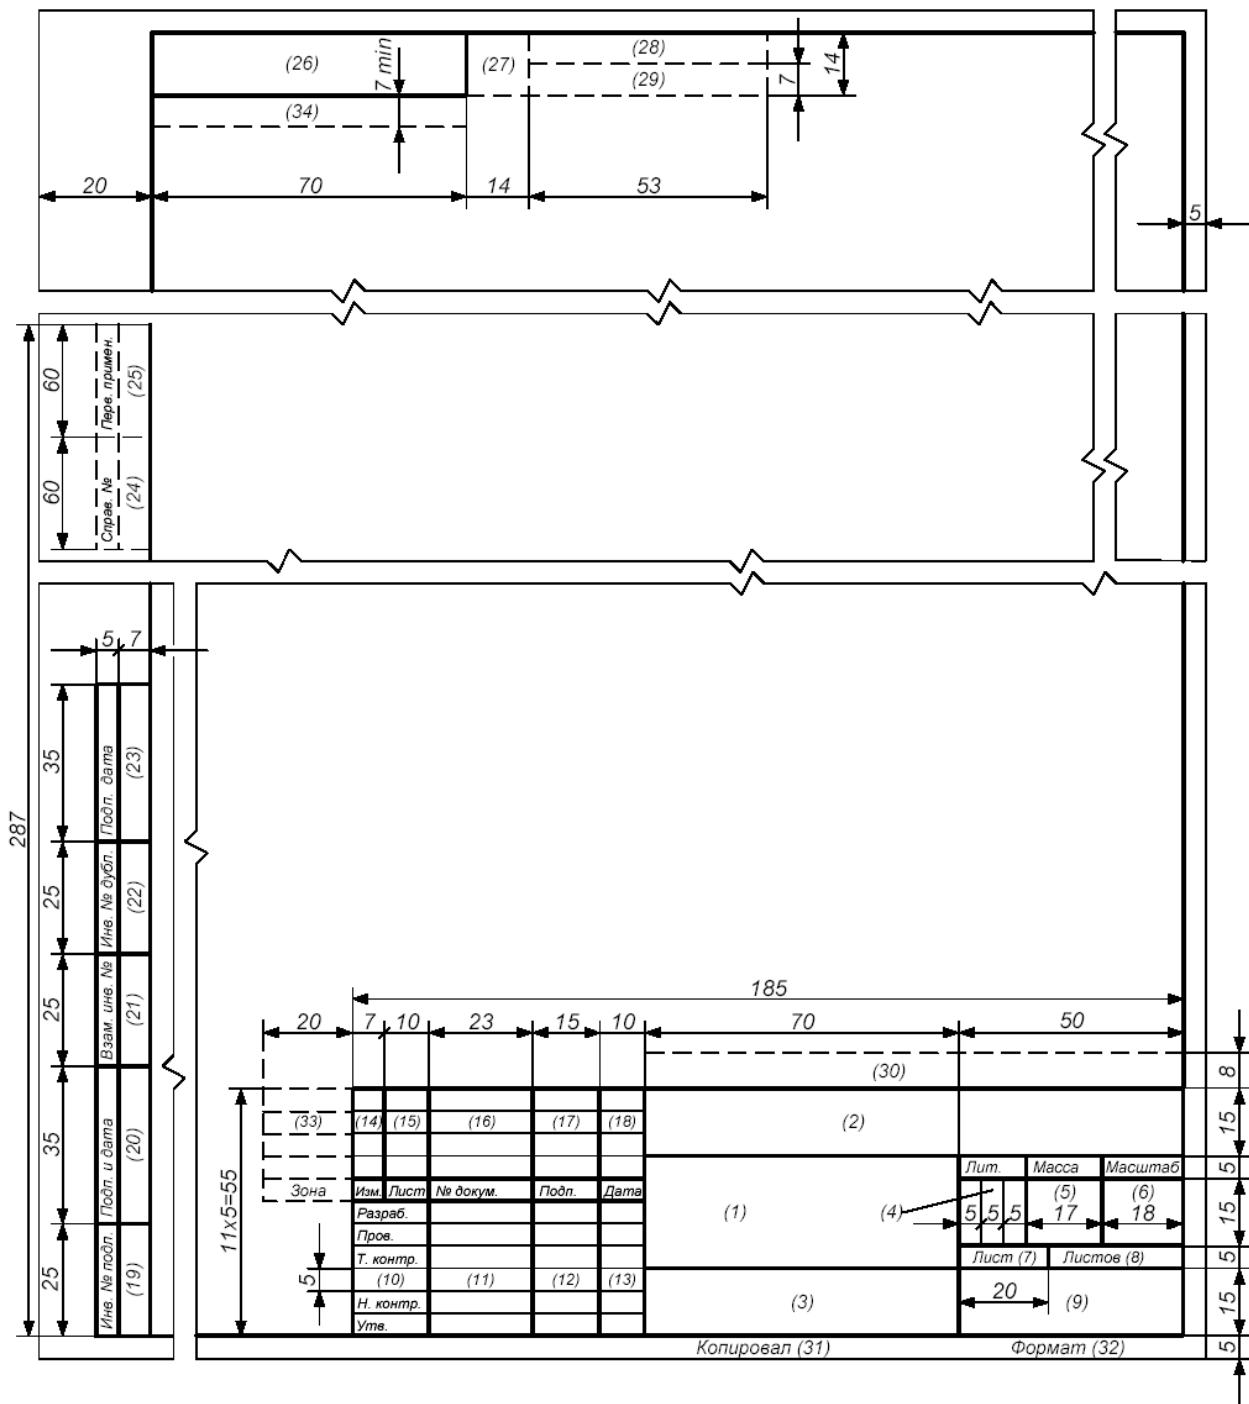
Форма 1. Основний напис для креслень та схем
